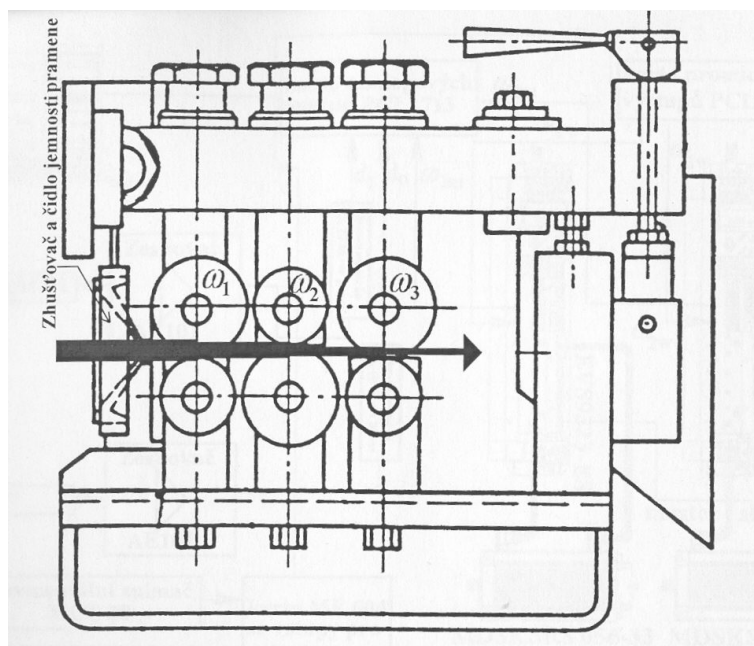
Zjednodušené schéma mykacího stroje typu Sliver Machine.
